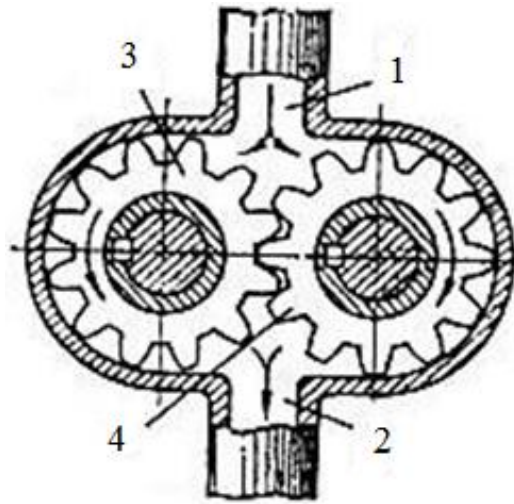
Шестеренний насос: 1 – всмоктувальний рукав; 2 – напірний рукав; 3 – ведуча шестерня; 4 – ведена шестерня.
